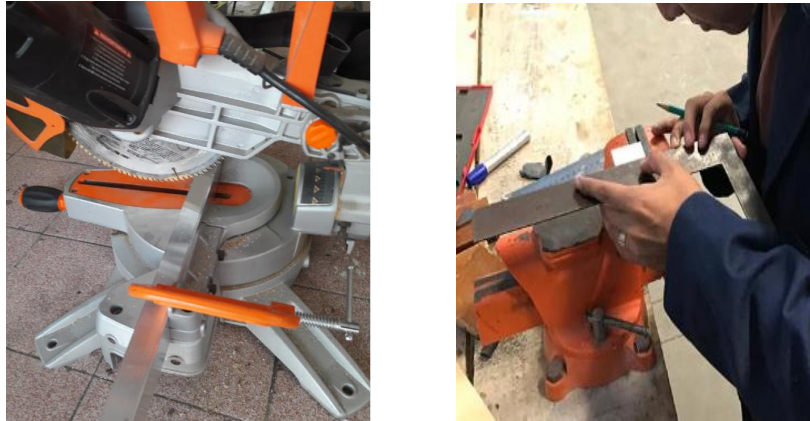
Corte de aluminio y trazado en piezas de aluminio.
